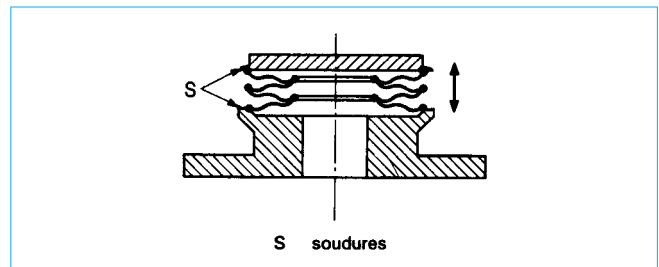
Étanchéité par soufflet à disques soudés
